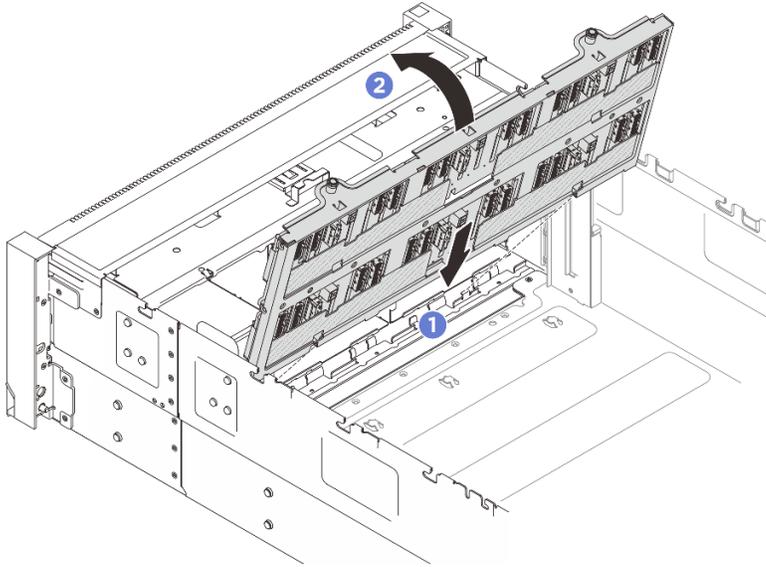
Installation d'un support de fond de panier d'unité (châssis doté d'une baie 2,5 pouces)
